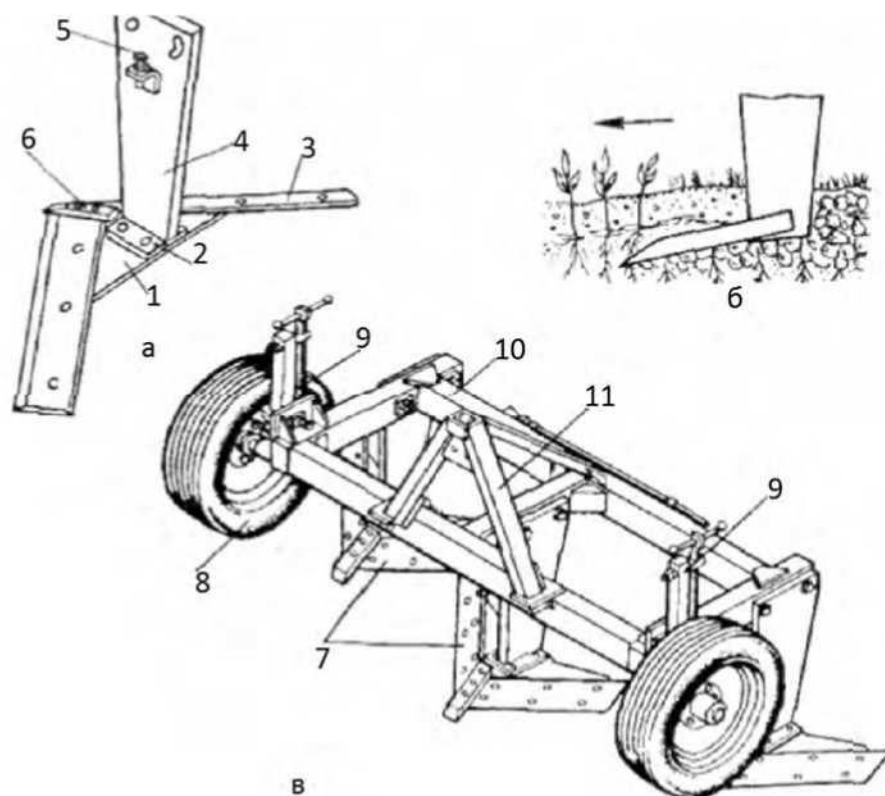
Органы для основной безотвальной обработки почвы: а – стреловидная плоскорежущая лапа; б – лемех; в – плоскорез-глубокорыхлитель
